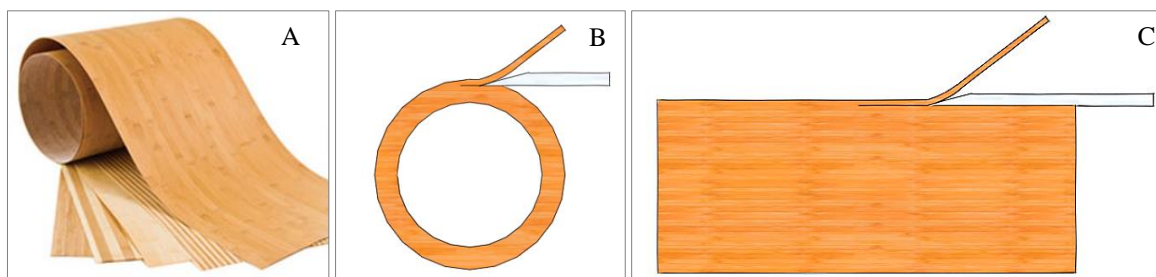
Lâmina de bambu (A); Torneamento do colmo(B); Faqueamento de placas de bambu laminado colado (C)
